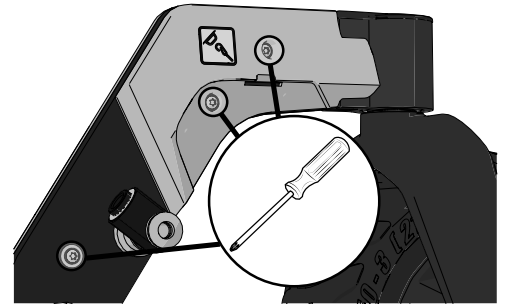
Ermitteln Sie die Position der drei Schrauben.
